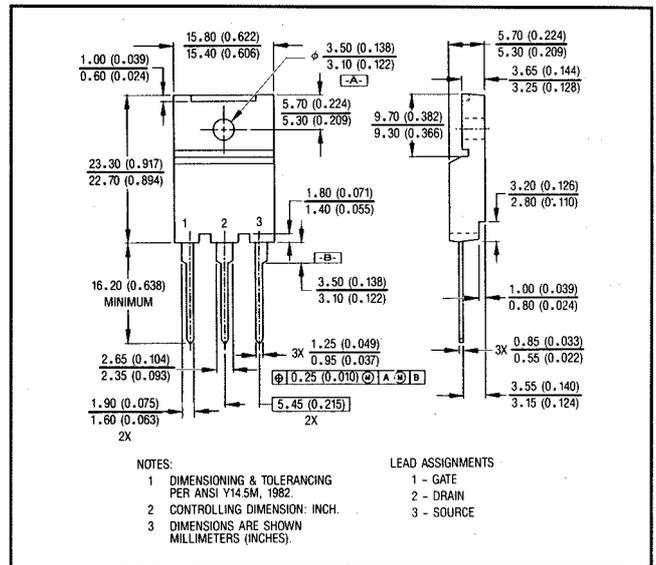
Полностью изолированный пластмассовый корпус Full Pak типа TO-247
